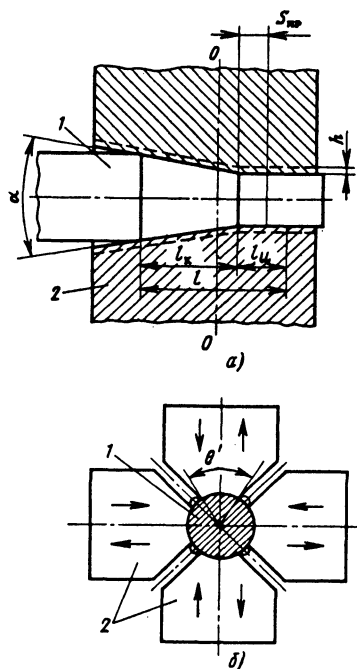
Инструмент и заготовка при ротационной ковке: а - сечение в направлении продольной оси заготовки; б - поперечное сечение; 1 - заготовка; 2 - бойки; 3 - область пластической деформации; $l_{ц}$ - калибрующий участок; h - радиальное обжатие; θ' - рабочий участок бойка
